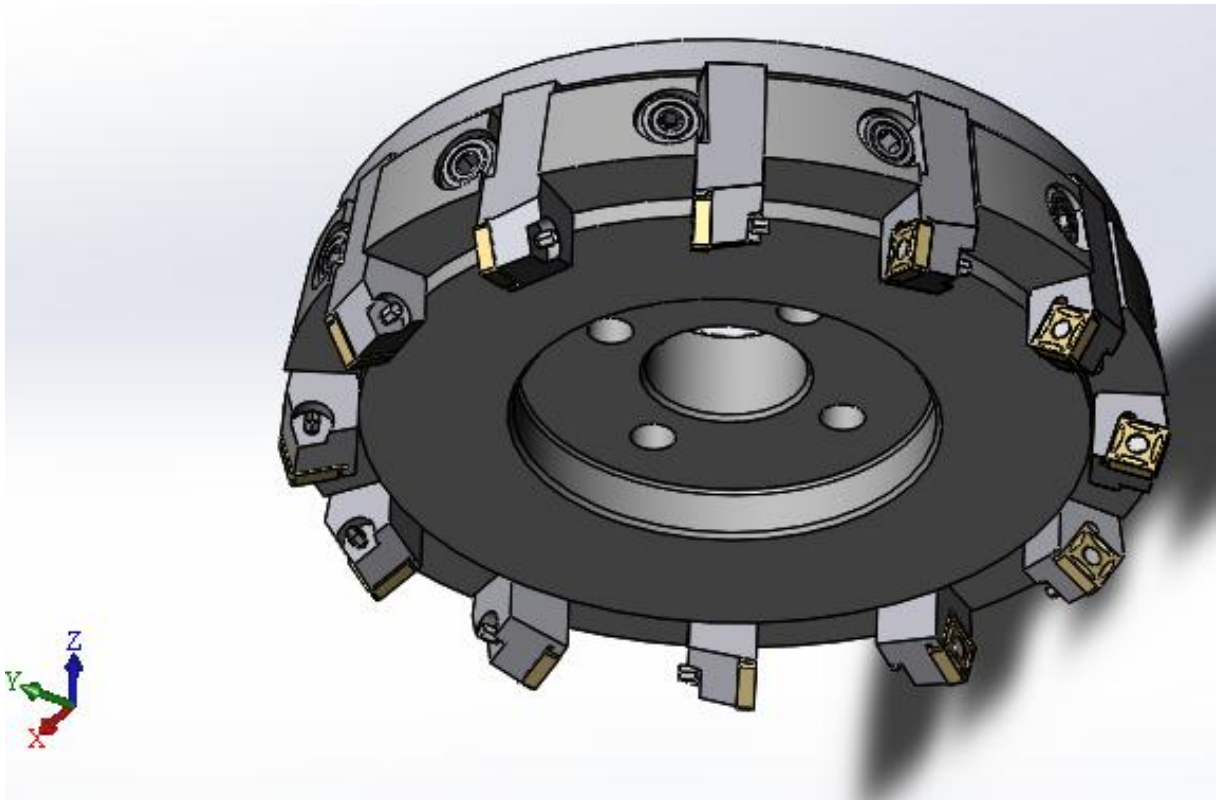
3D-модель фрези в SolidWorks з квадратною пластиною
